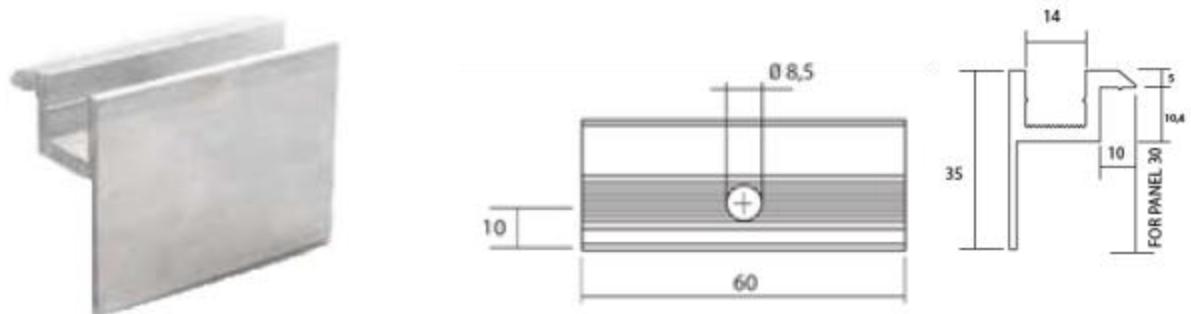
Brides latérales – Cadre du module de hauteur 30 mm
